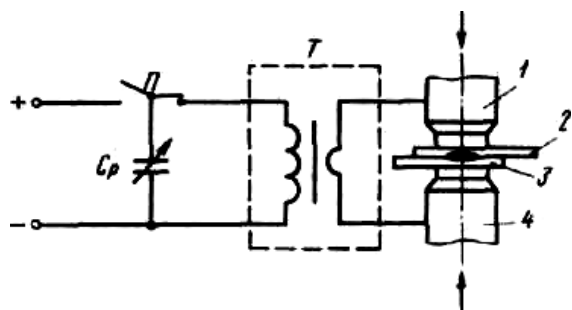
Схема нагрева деталей при конденсаторной сварке
